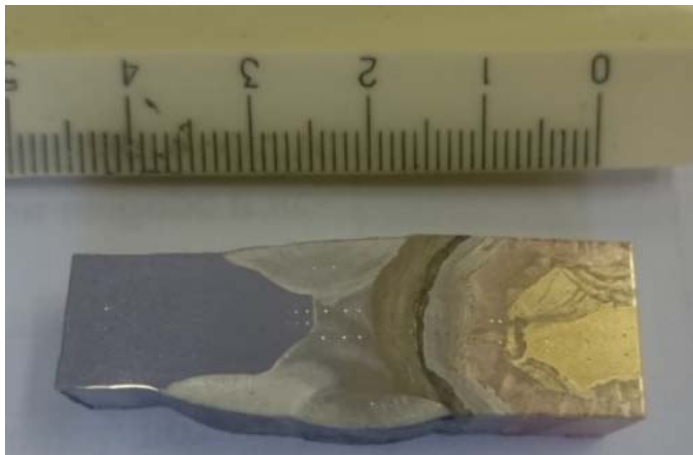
Макрошлиф сварного соединения азотсодержащей стали 04X20H6Г11М2АФБ с алюминиевой бронзой БрАМц9-2.
